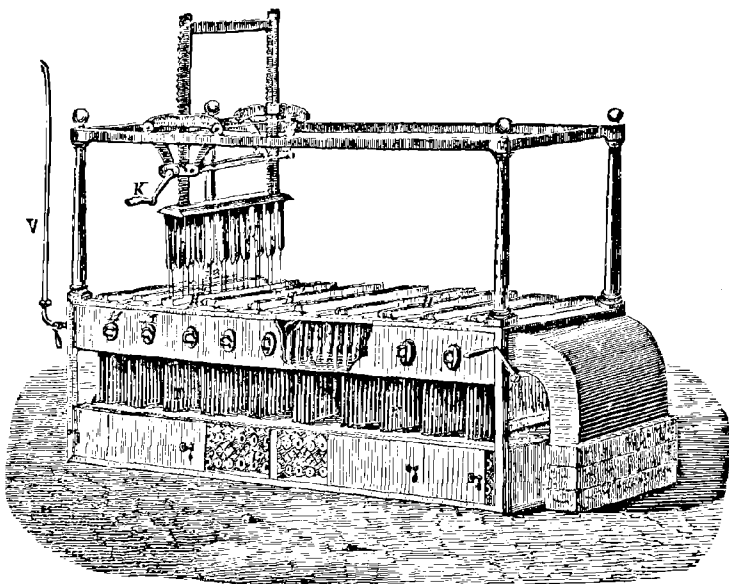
Machine pour le moulage continu des bougies, avec chauffage par la vapeur et refroidissement par ventilation.
